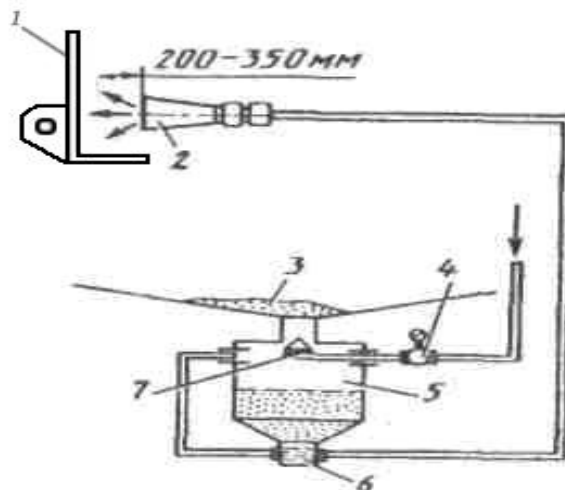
Схема дробоструминної обробки в камері: 1 - книця; 2 - сопло; 3 - збірник дроби; 4 - редуктор-манометр; 5 - робочий бункер; 6, - приймальний штуцер; 7 - перепускний клапан
